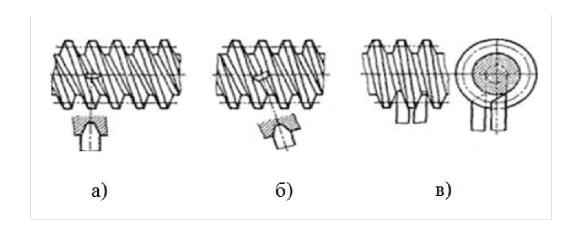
Классификация червячных передач по форме боковой (рабочей) поверхности витка червяка
